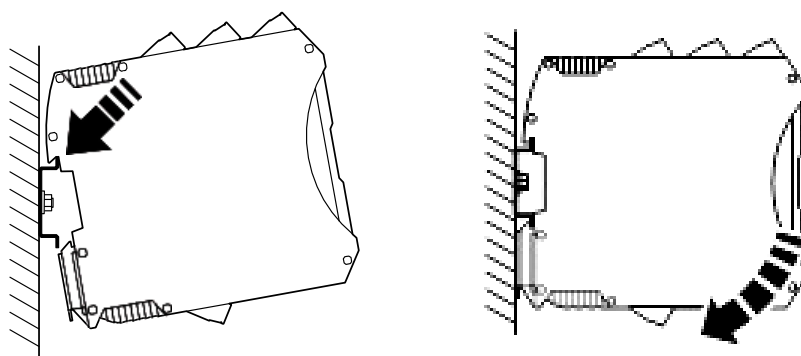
Схема монтажа модулей на шинные соединители
